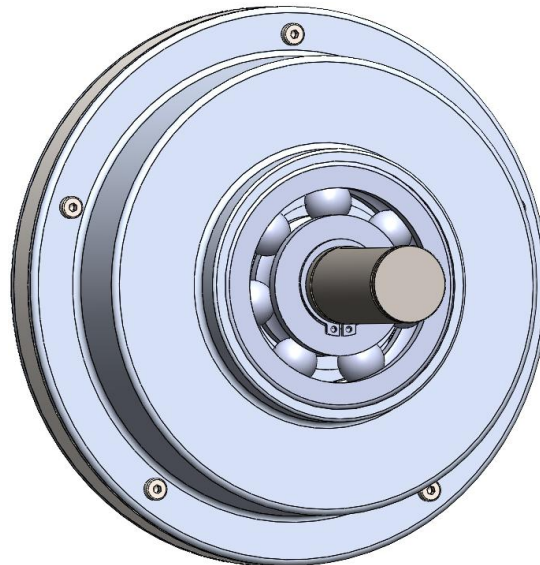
Vista desde el eje de salida del ensamblaje CAD 3D de la caja de engranajes con la carcasa.
